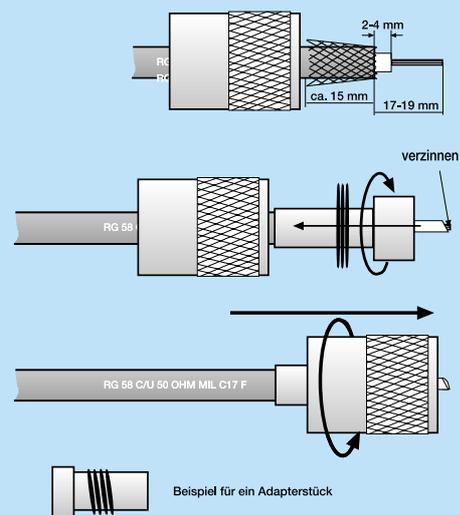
Montagebeispiel für PL-Stecker mit Schraubmontage
